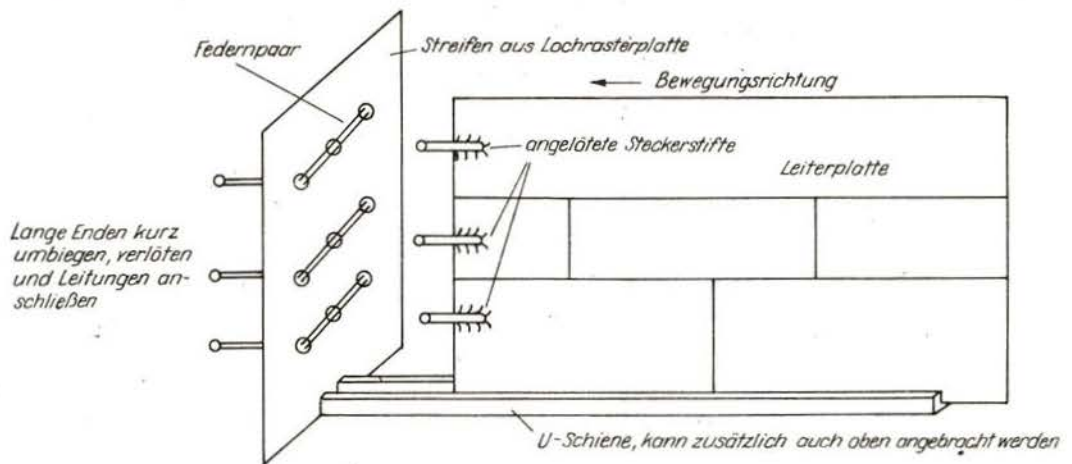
Prinzip der Steckverbindung der Leiterplatten
